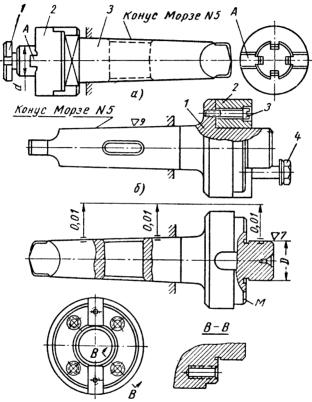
Оправки для крепления фрез: a — для фрез диаметром от 40 до 110 мм;  $\emph{6}$  — для фрез диаметром от 150 до 400 мм
